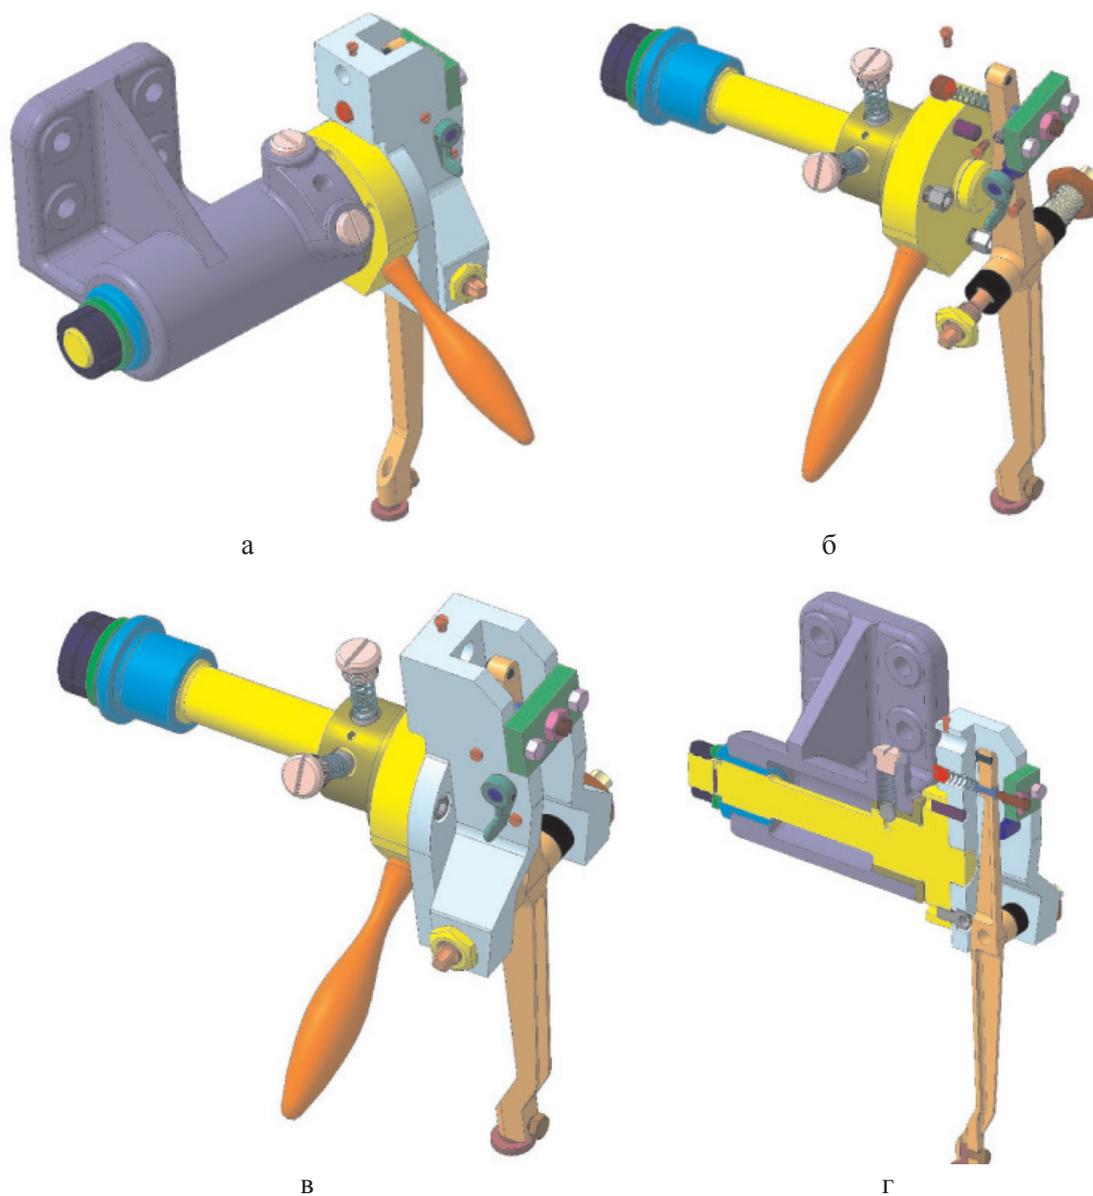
3D сборка приспособления для проверки биения торца блока шестерен
